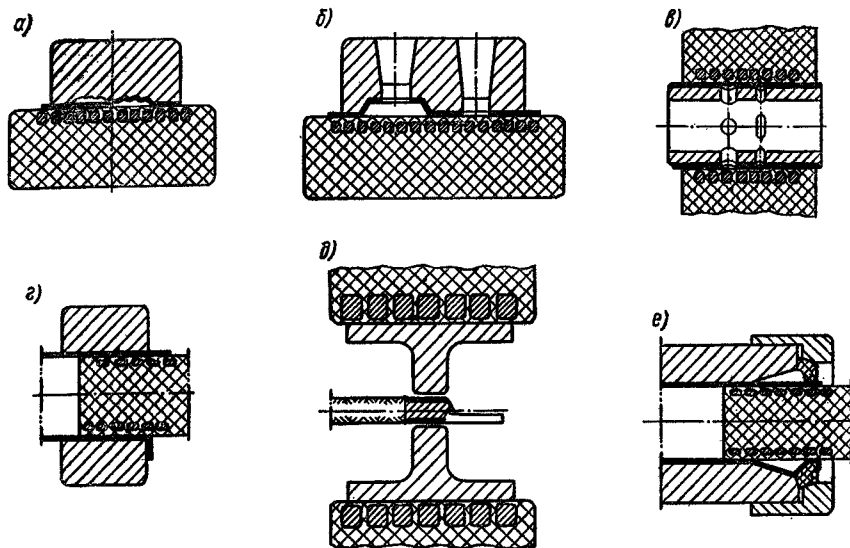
Различные операции, выполняемые магнитно-импульсной штамповкой: а — формовка; б — пробивка и отбортовка; в — пробивка отверстий; г — сборка с развальцовкой отбортовкой; д — обжатие кабельных наконечников; е — раздача трубы и сборка с фланцем
